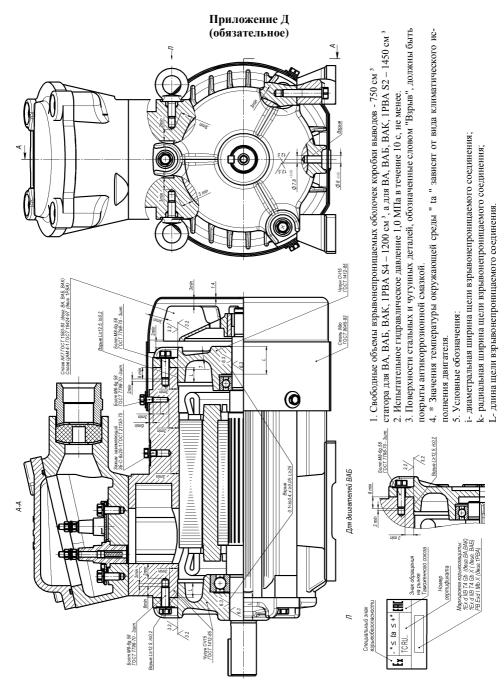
Чертеж средств взрывозащиты двигателя
